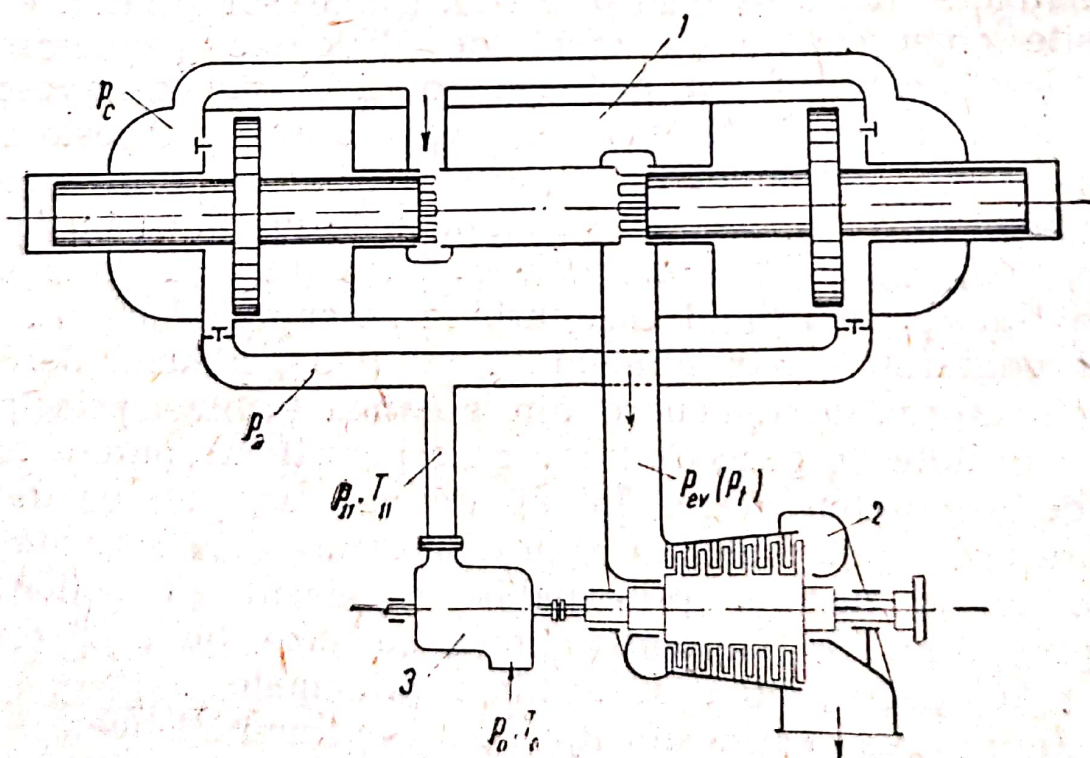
Schema supraalimentării cilindrului compresor. Compresorul de supraalimentare acționat prin turbină principală:
